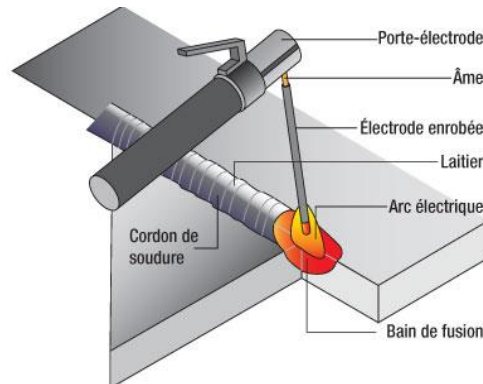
le soudage à l'électrode enrobée [7].
